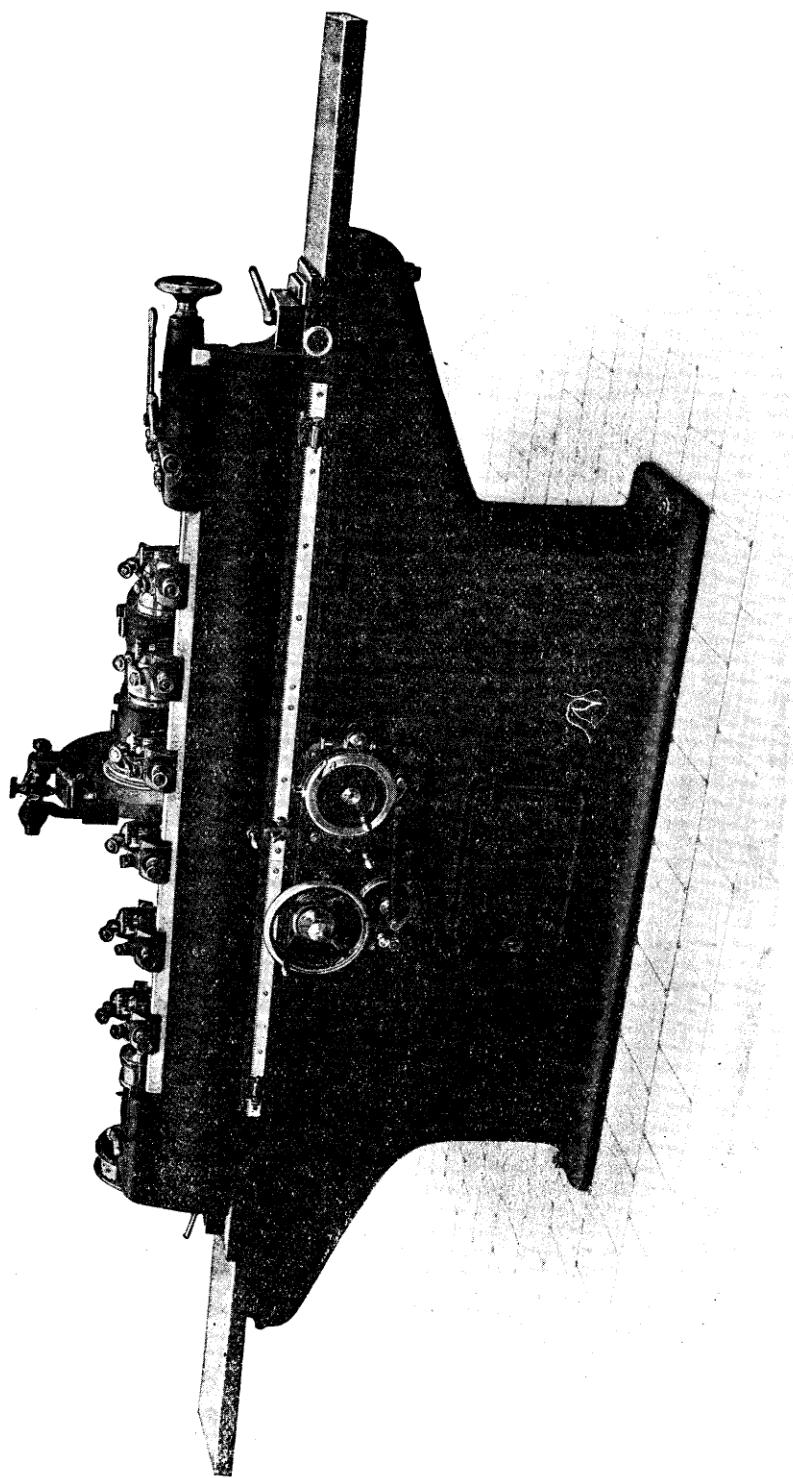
Machine de précision à rectifier les surfaces cylindriques et coniques.
